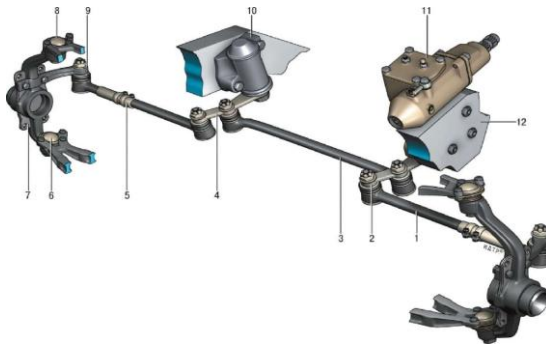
Рульовий привод з задньою трапецією і незалежною підвіскою (Chevrolet Niva): 1 - бічна тяга; 2 - сошка; 3 - середня тяга; 4 - маятниковий важіль; 5 - регульовальна муфта; 6 - кульова опора підвіски; 7 - правий поворотний кулак; 8 - кульовий шарнір підвіски; 9 - важіль правого поворотного кулака; 10 - кронштейн маятникового важеля; 11 - рульовий механізм; 12 - лонжерон кузова.
